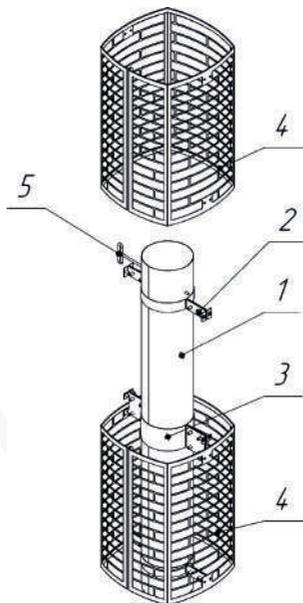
Схема сборки декоративно защитного ограждения дымохода Сударушка Чистопар
